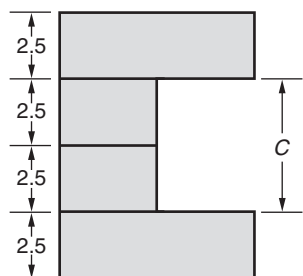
Ensamble para el problema 44.8 (dimensiones en cm).
